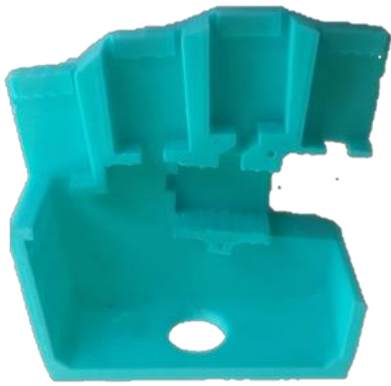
Impresión 3D, material PLA, de palma de la mano.
